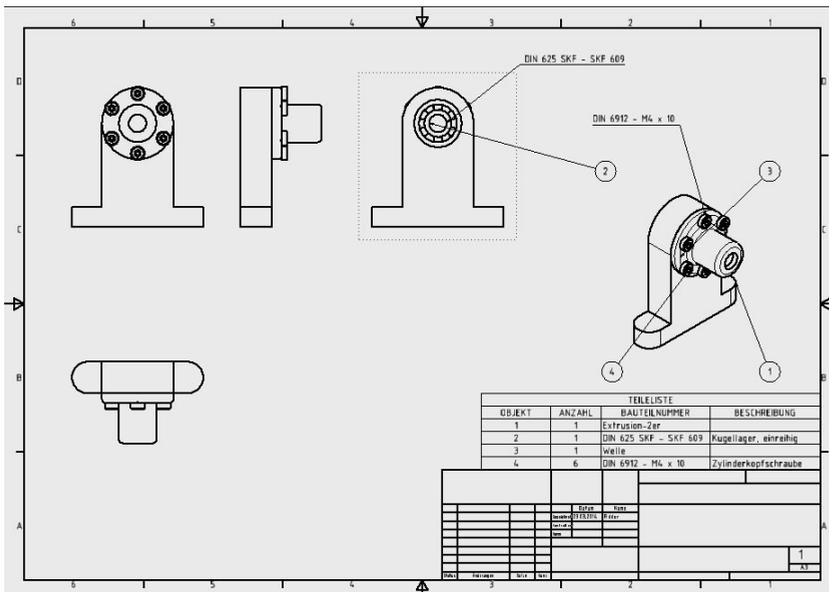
Zeichnung für eine Baugruppe mit Stückliste und Positionsnummern
